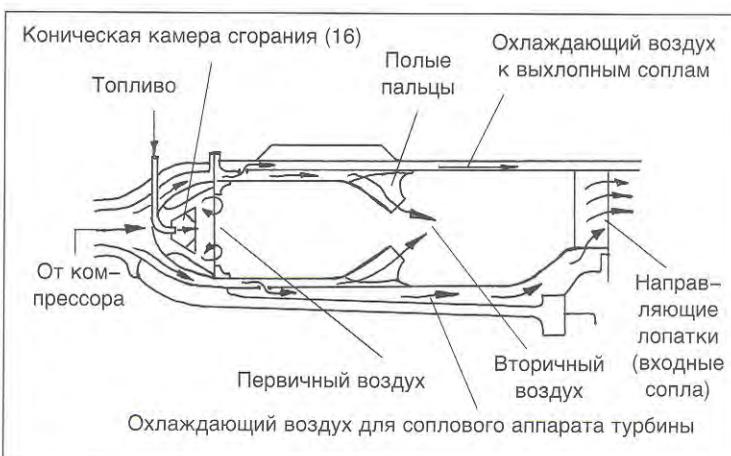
Эскиз камеры сгорания двигателя BMW 109-003
